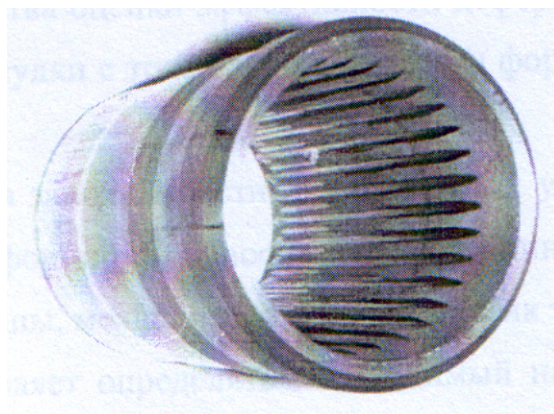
Заготовка шліцьового з'єднання карданного валу дизель-потягу ДП 2
